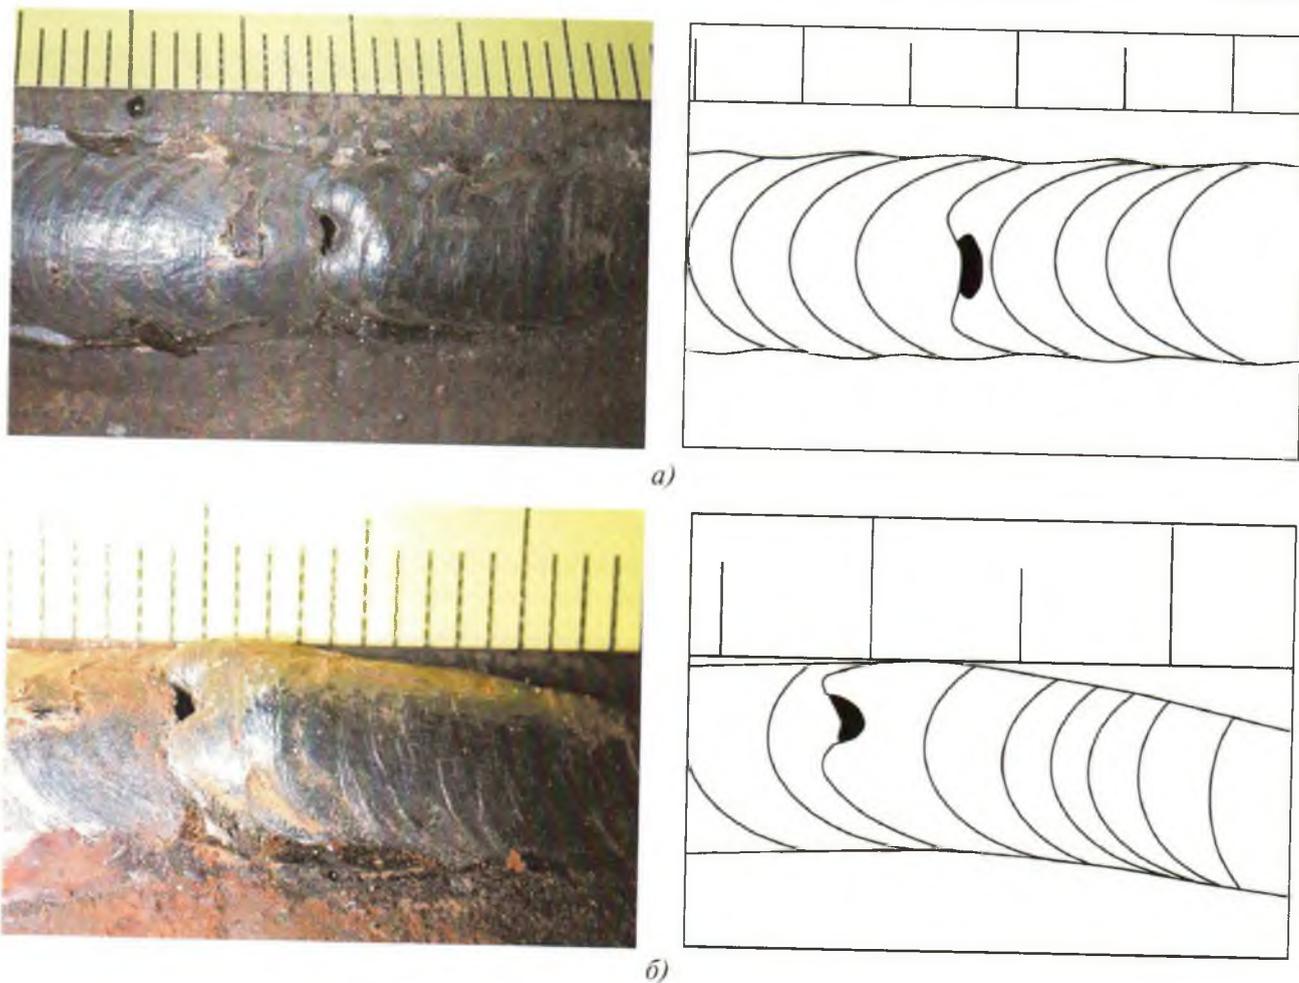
Непровар – несплавление между чешуйками валика – на лицевой поверхности шва в стыковом сварном соединении трубопровода:
